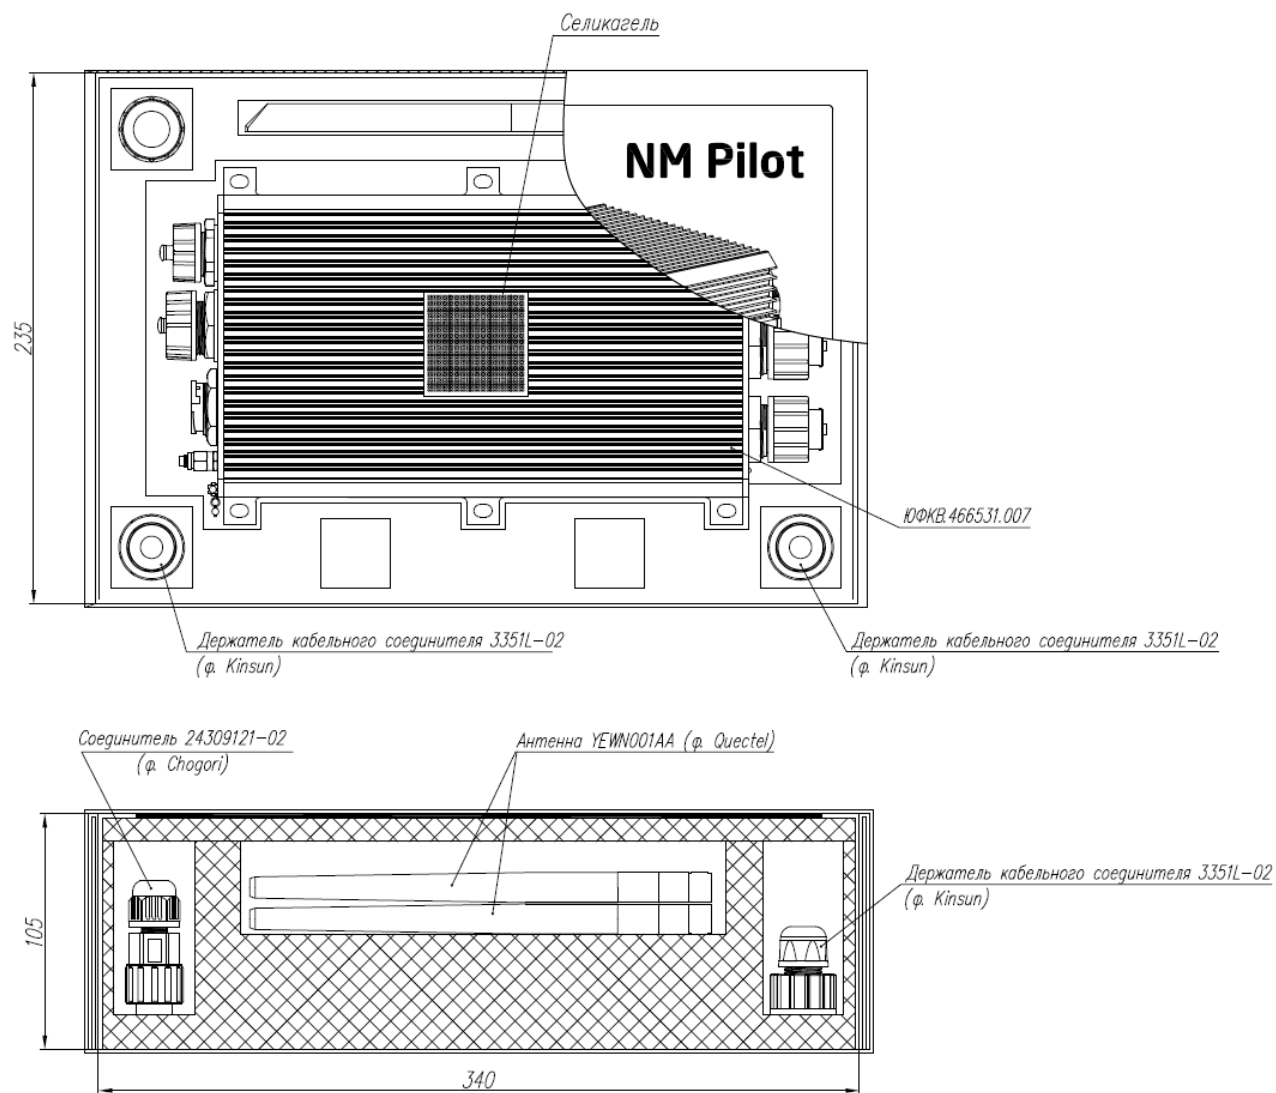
Габаритные размеры упаковки Изделия
